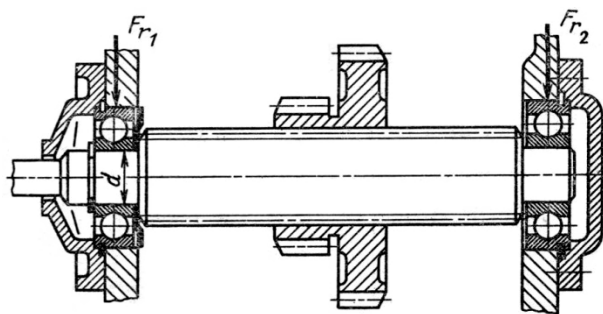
Подшипниковые узлы шлицевого вала коробки передач
